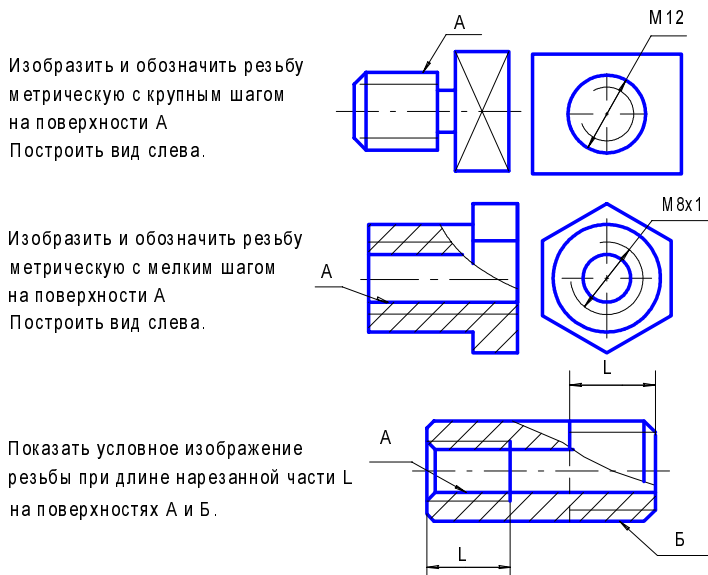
Пример изображения и обозначения метрической резьбы
